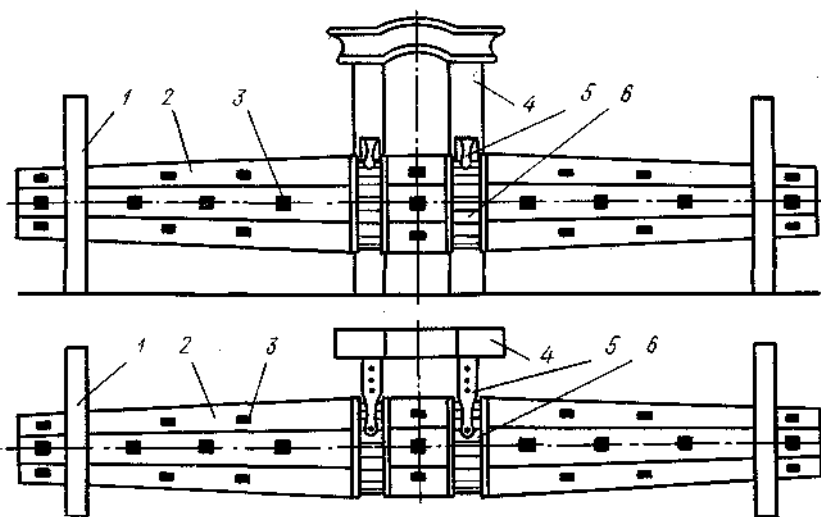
Брашпиль XVIII в.: 1 — битенги; 2 — барабан; 3 — шпильгаты; 4 — траверза; 5 — палы; 6 — зубчатые колеса
